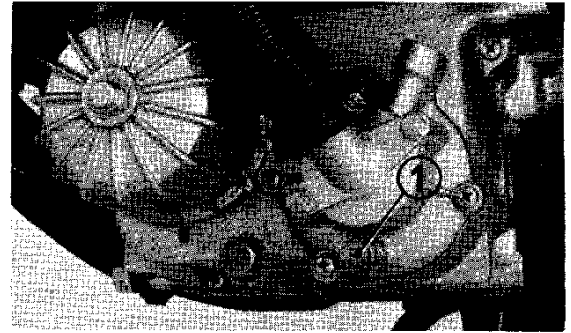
(1) Kühlmittel-Ablafschraube
